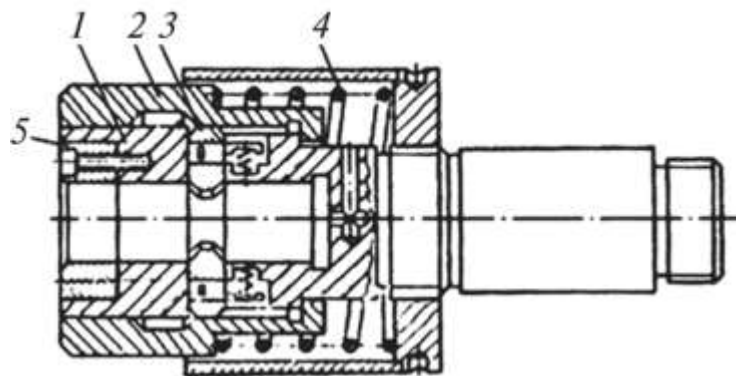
Схема автоматичного робочого патрона для горизонтально-протяжного верстата
